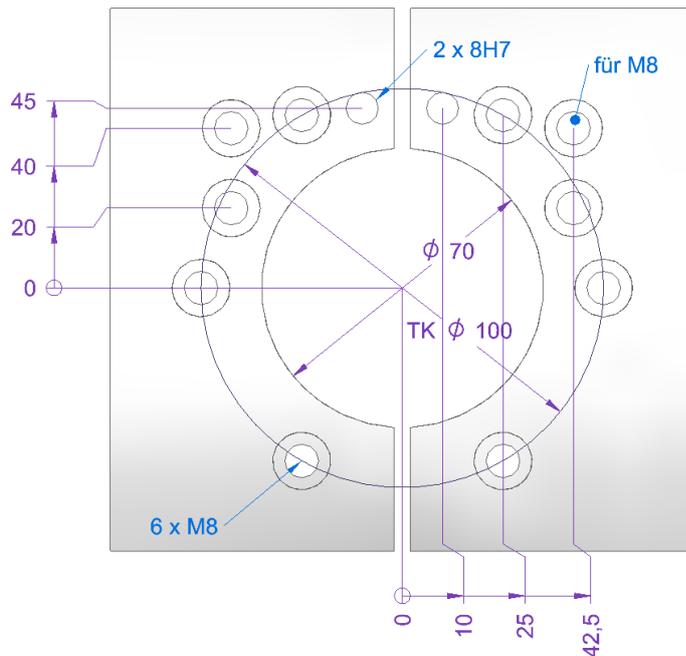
Maße aktueller Anschlussflansch Z-Schlitten für Extruder
